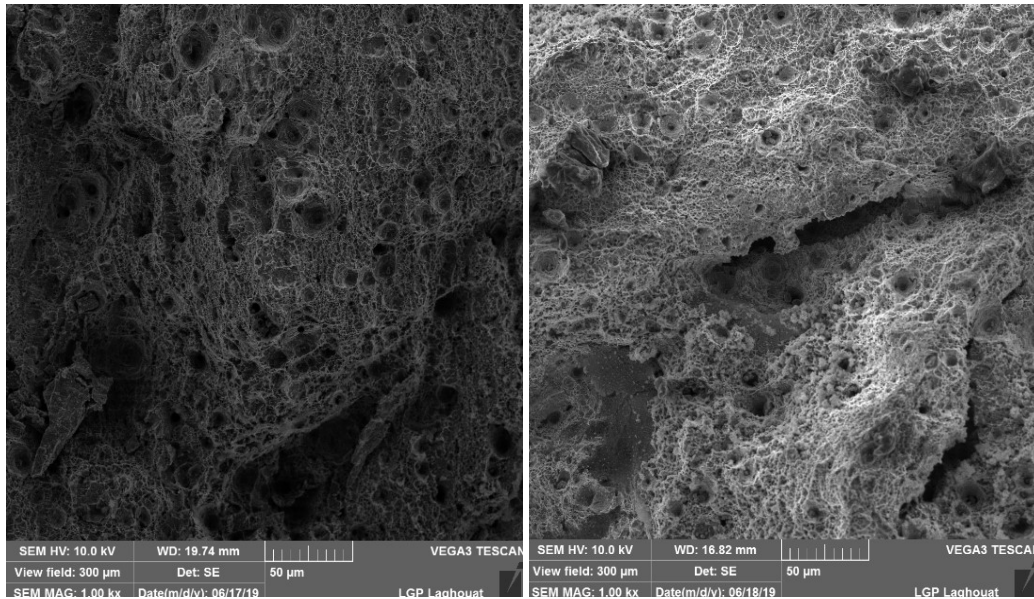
Fractographies des éprouvettes soudée sans traitement thermique, a) avant et b) après le traitement de vieillissement
